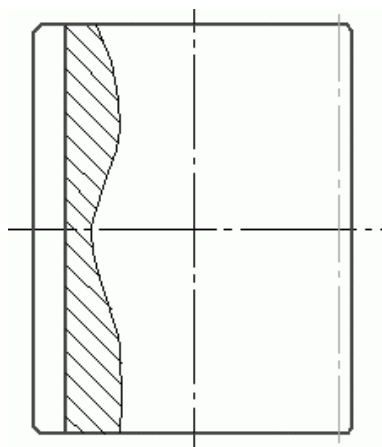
Полученная зубчатая шестерня (слой с изображением зубчатого колеса погашен)
